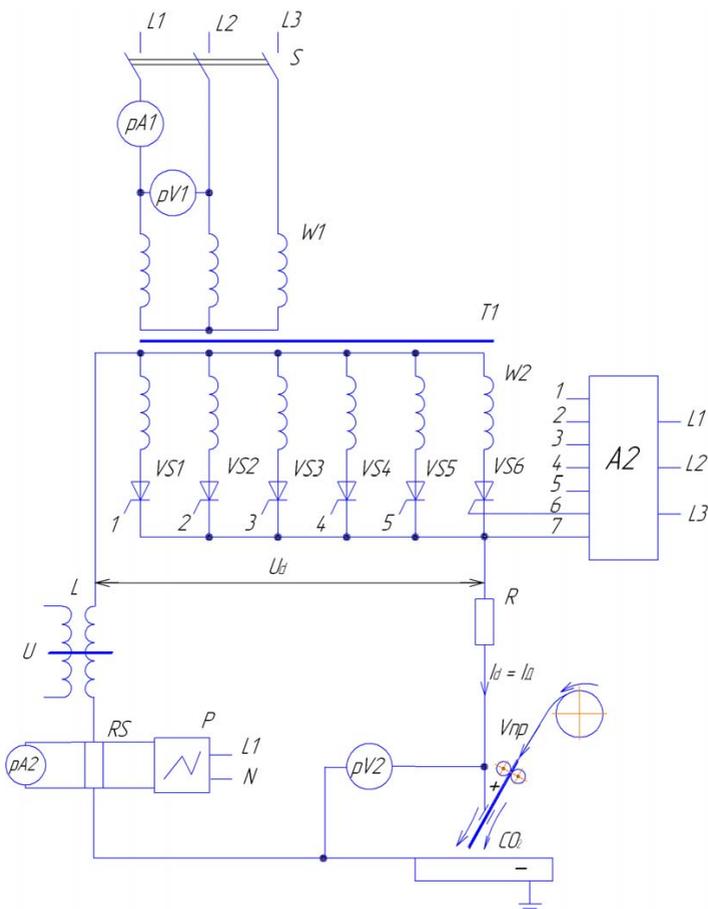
Принципиальная схема сварочного выпрямителя ВСП-160:
